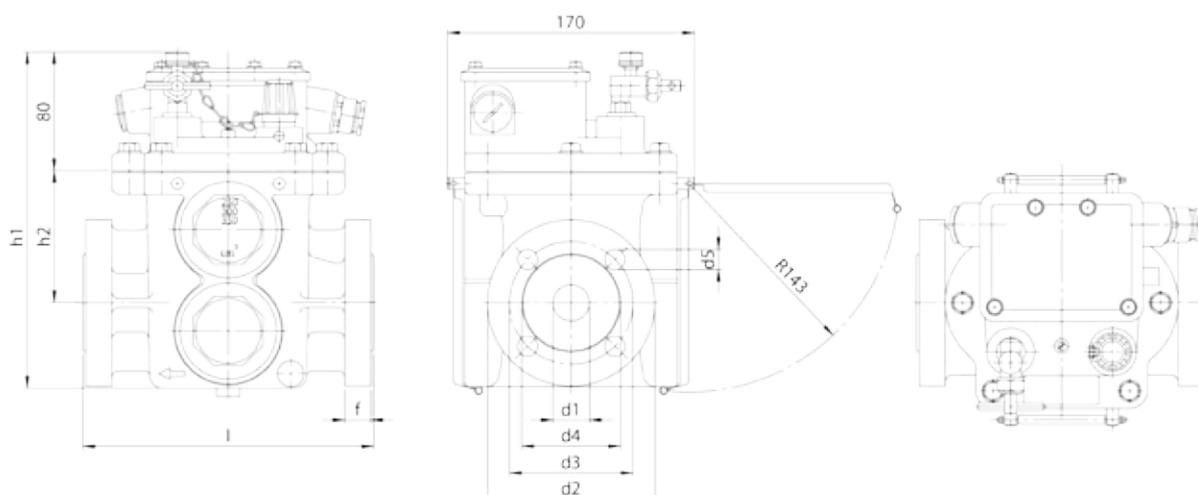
Размерный эскиз типов 05, 06, 07, 08, 09, 24
